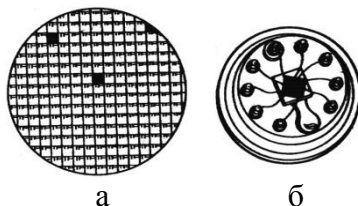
НІМС: а) підкладка; б) з'єднання із зовнішніми виводами корпусу
